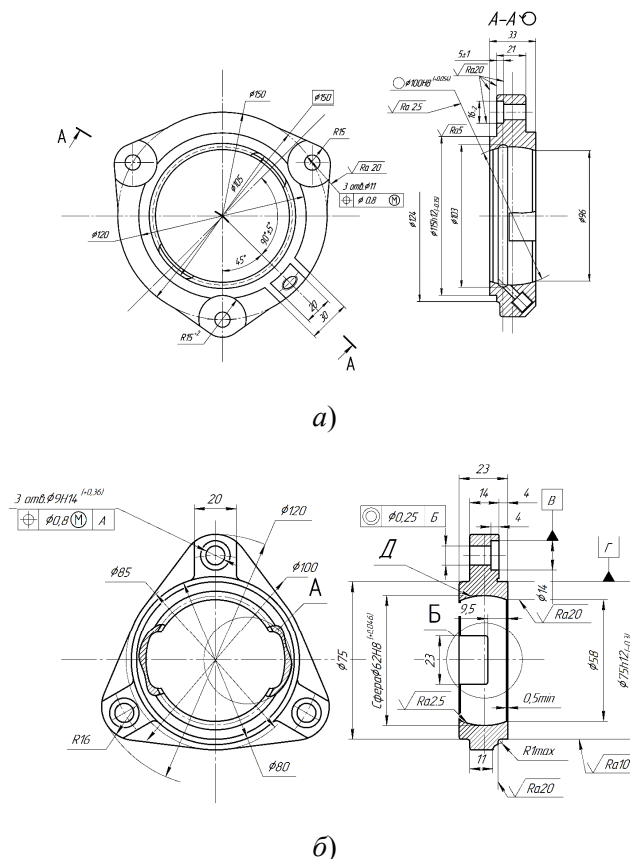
Эскизы деталей КЗК-10-0290105 (а), КЗР 010105 (б)
